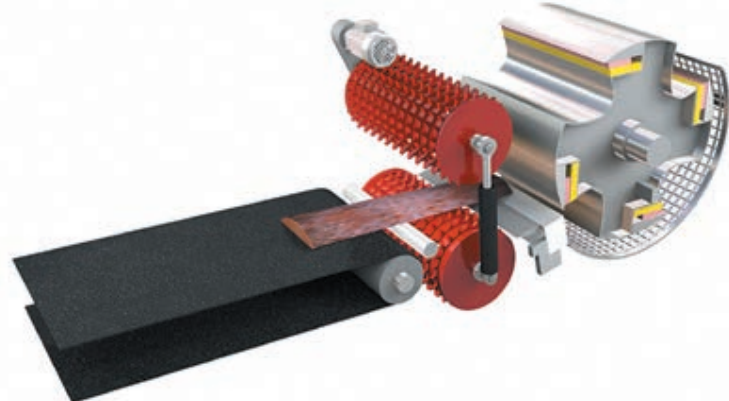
Схема рубильной машины на базе ножевого вала со сменными ножами
